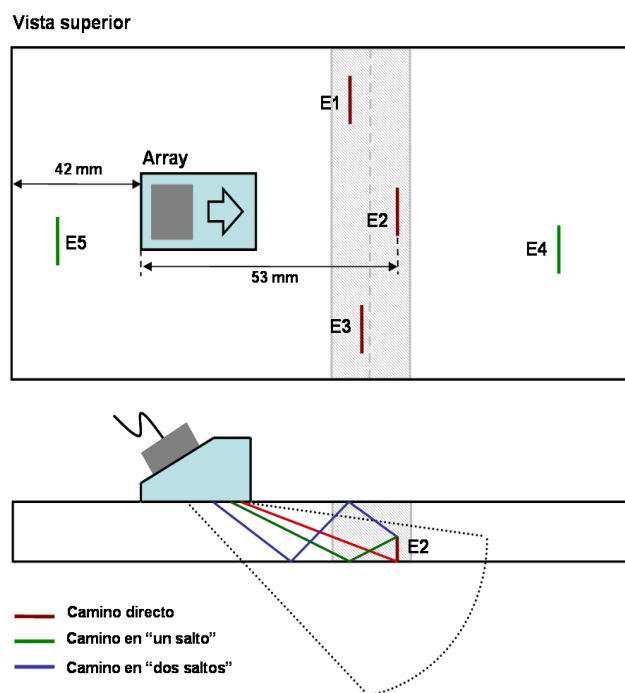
Esquema de la inspección de la entalla 2 a través de la soldadura. (arriba) Vista superior con la ubicación del array en la pieza (abajo) sección transversal con la zona de la imagen en línea de puntos y los tres posibles caminos del haz ultrasónico hasta la entalla.
